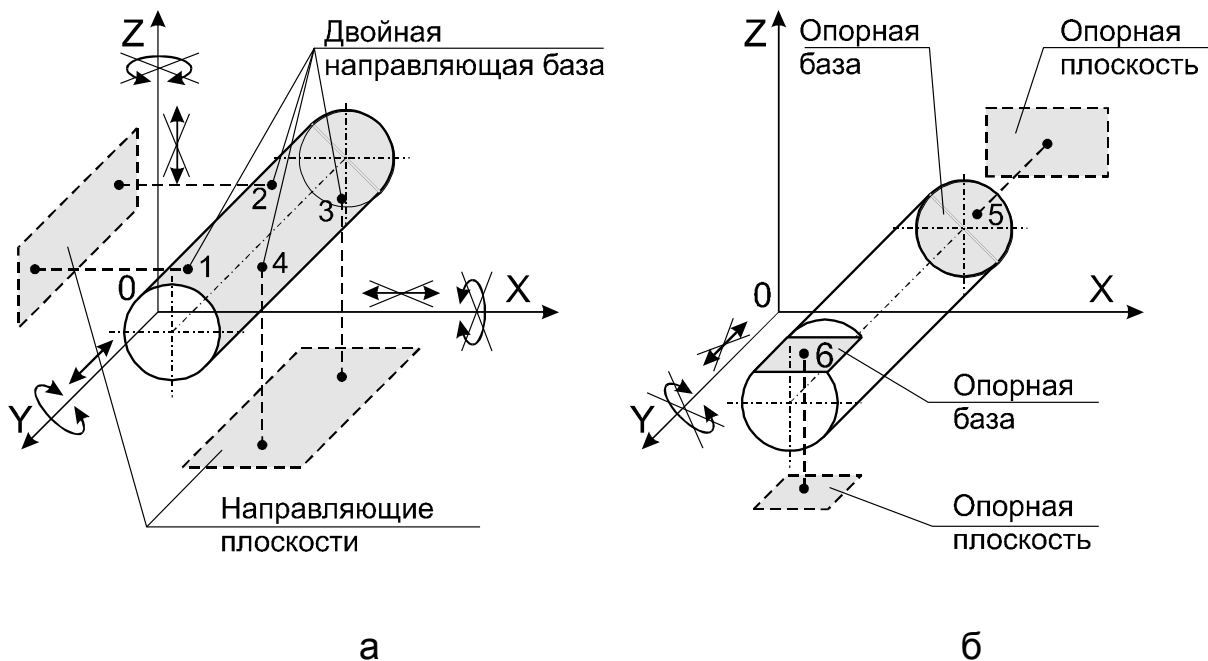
Комплект баз цилиндрической заготовки:
